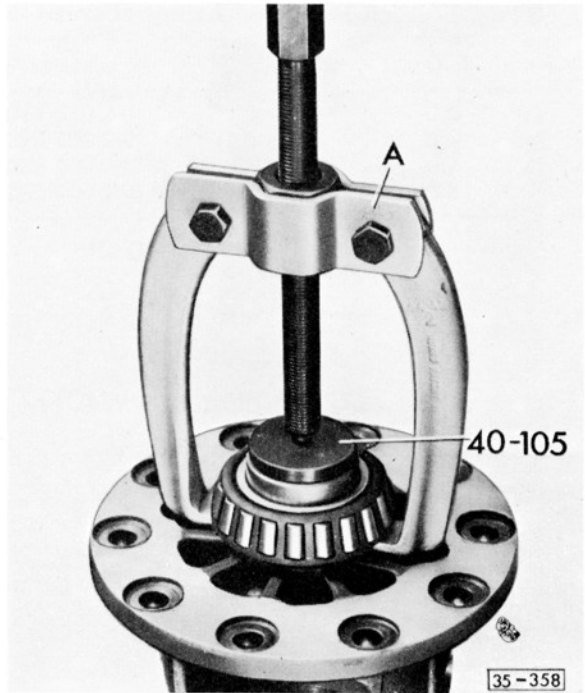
Innenring für großes Kegelrollenlager vom Gehäuse abziehen:
